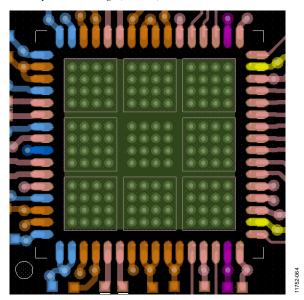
AD9680 のエクスポーズド・パッドに対する推奨 PCB レ イアウト
